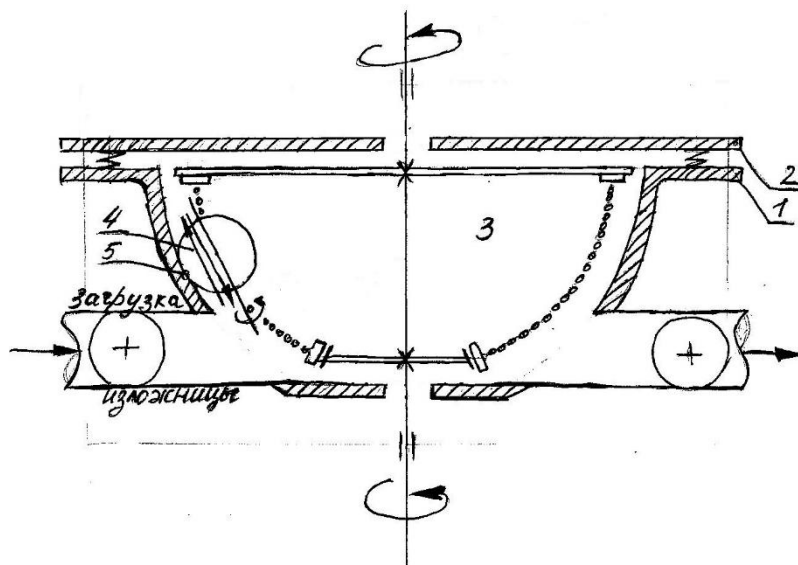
Схема лабораторной установки сложного движения сферической изложницы с изменяющейся длиной толкателя
